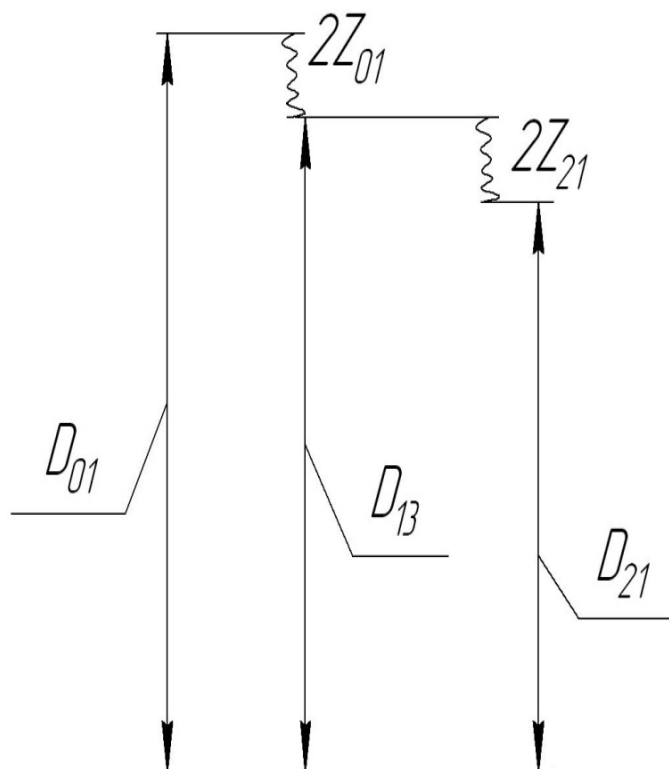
Размерная схема обработки поверхности $\varnothing 146_{-1}$
